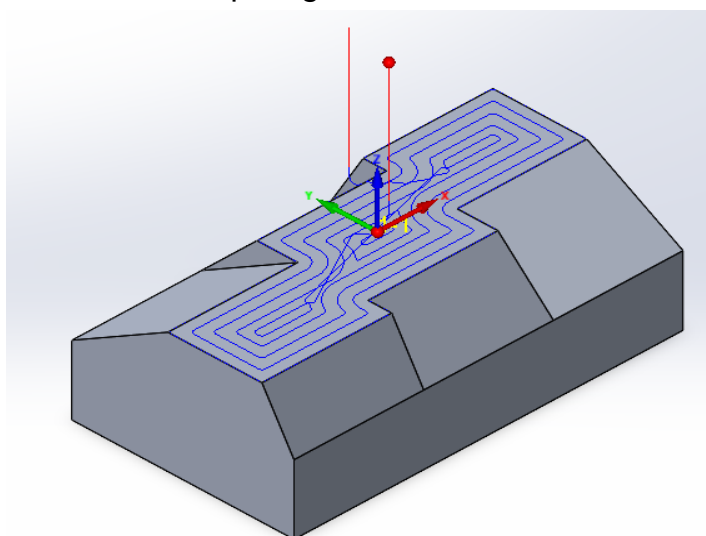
Trajetória executada durante a operação de maquinagem horizontal HSM
